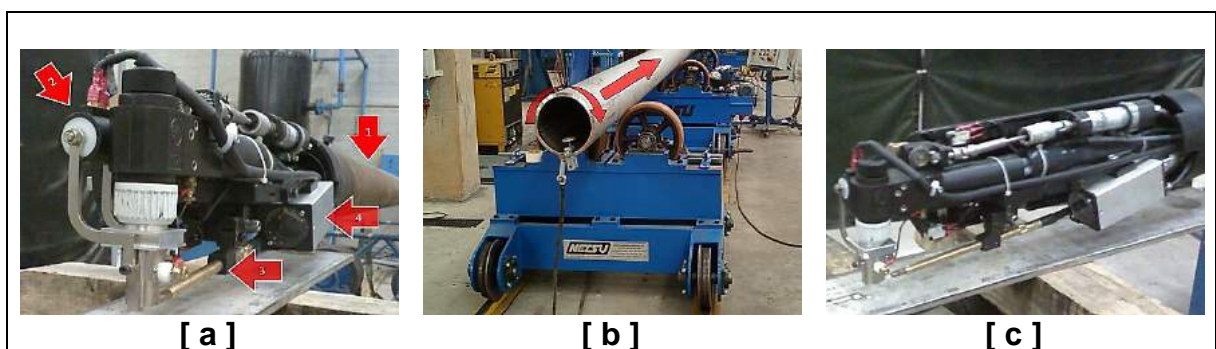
Equipamento de soldagem: [a] lança, tocha, bobina, hotwire e câmera, [b] carro de movimentos combinados (rotação e translação), [c] visão lateral da tocha
